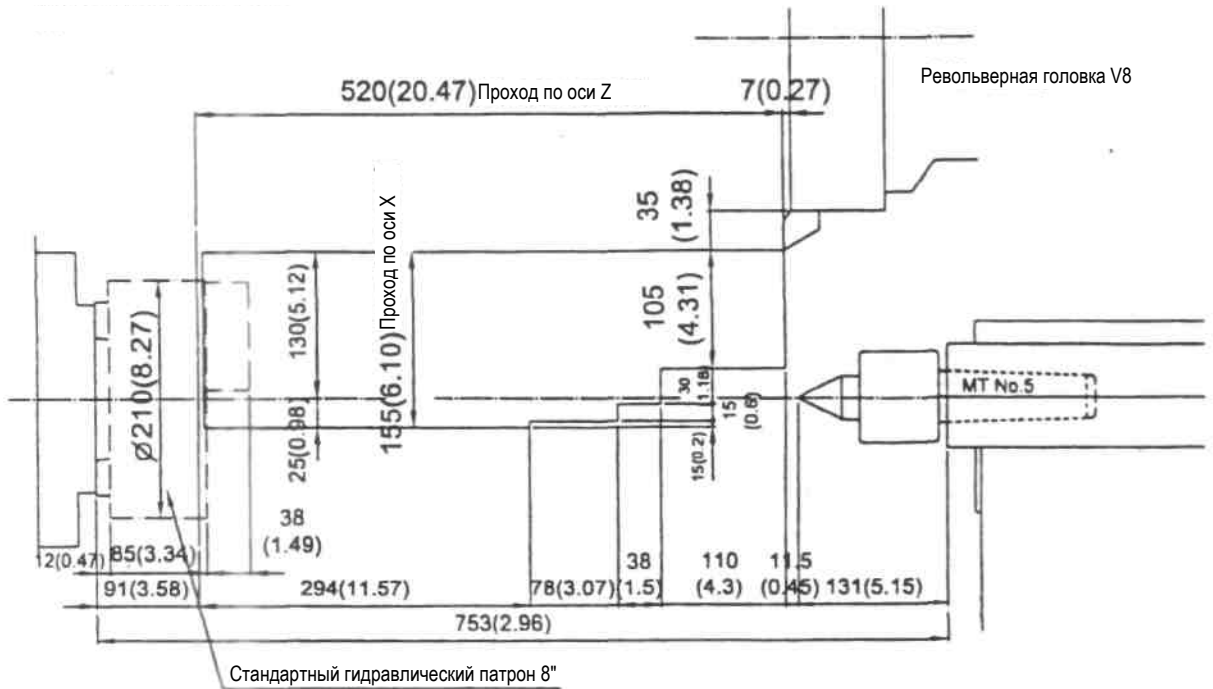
Схема рабочего диапазона (для прямого резцедержателя)
